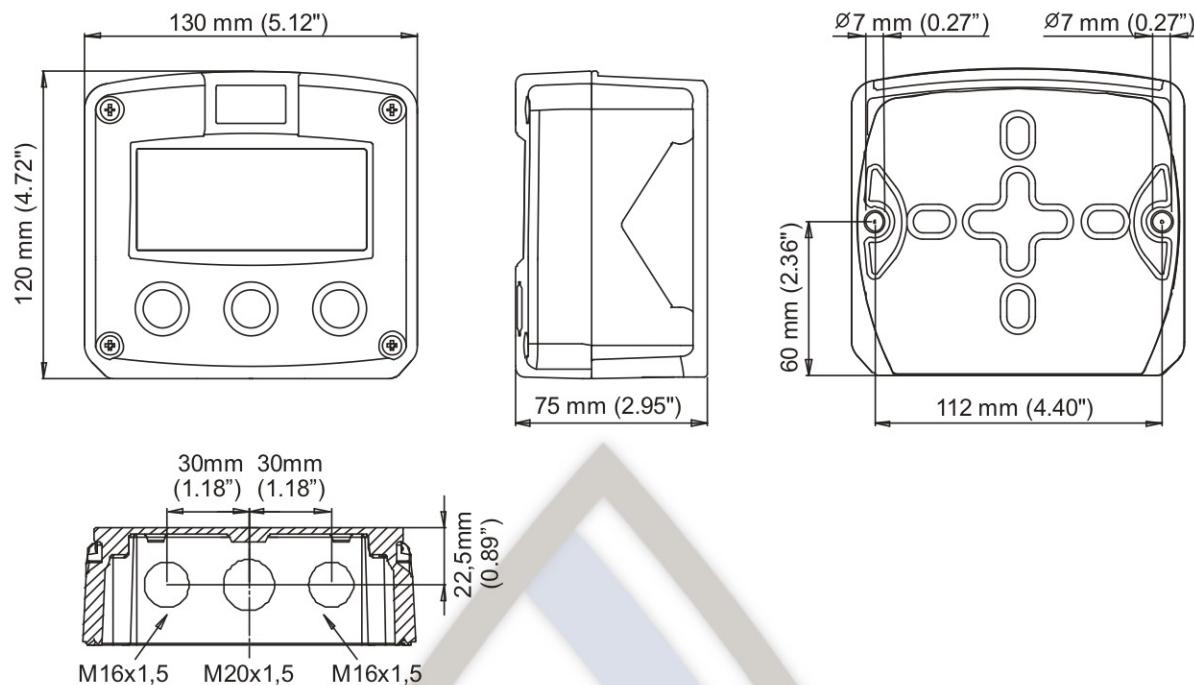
IP67 алюминиевый-магнитопроводящий корпус тип HM с 2 x M16 и 1 x M20- резьбовыми отверстиями
